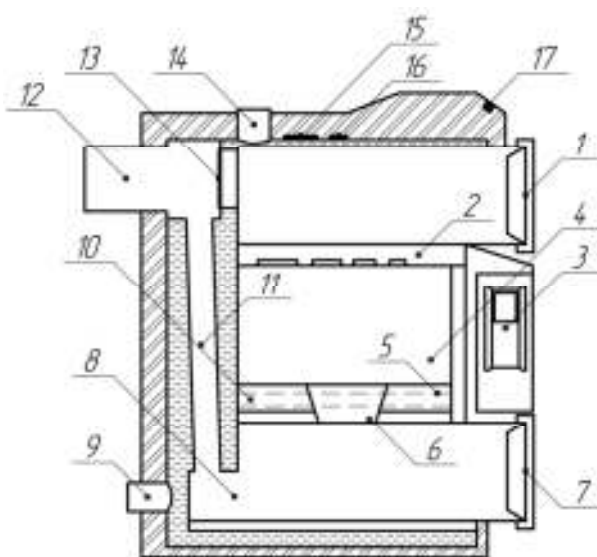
Будова піролізного котла: 1 – дверці для завантаження; 2 – канал подачі повітря; 3 – вентилятор; 4 – топка; 5 – водяний теплообмінник; 6 – форсунка; 7 – дверці для очищення котла; 8 – камера спалювання піролізних газів; 9 – патрубок зворотної подачі води; 10 – канал подачі вторинного повітря; 11 – канал відведення диму; 12 – боров; 13 – дросель димоходу; 14 – патрубок подачі води; 15 – датчик температури; 16 – датчик тиску; 17 – регулятор температури
